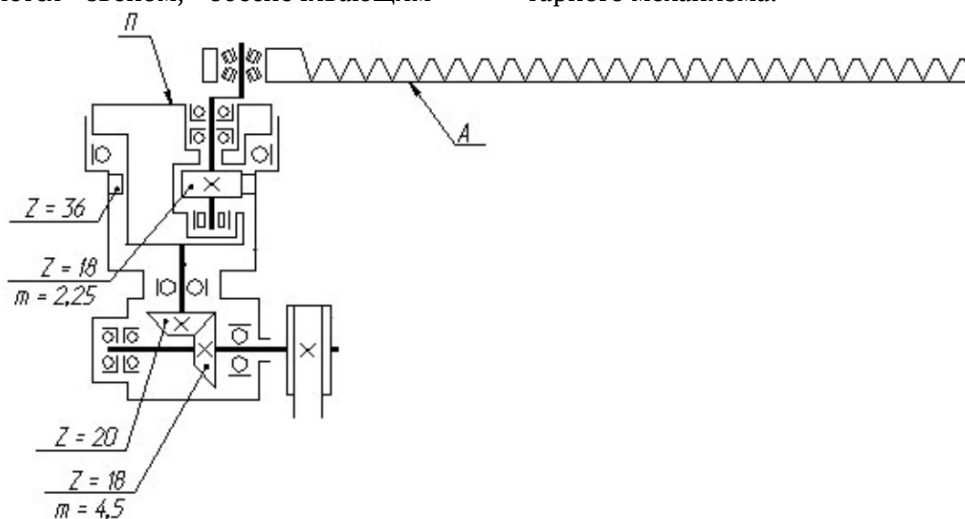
Кинематическая схема привода режущего аппарата жатки:
